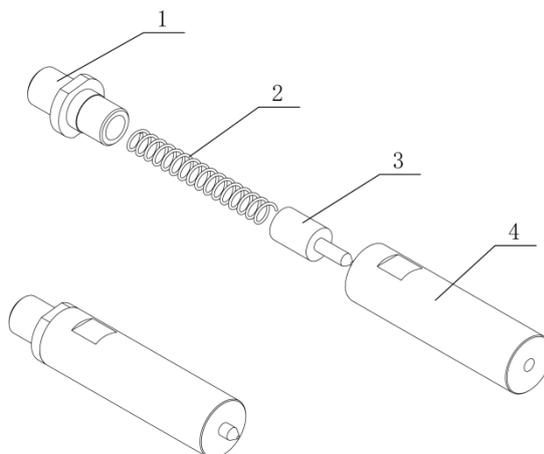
Нижний инструмент для шпилек и втулок
